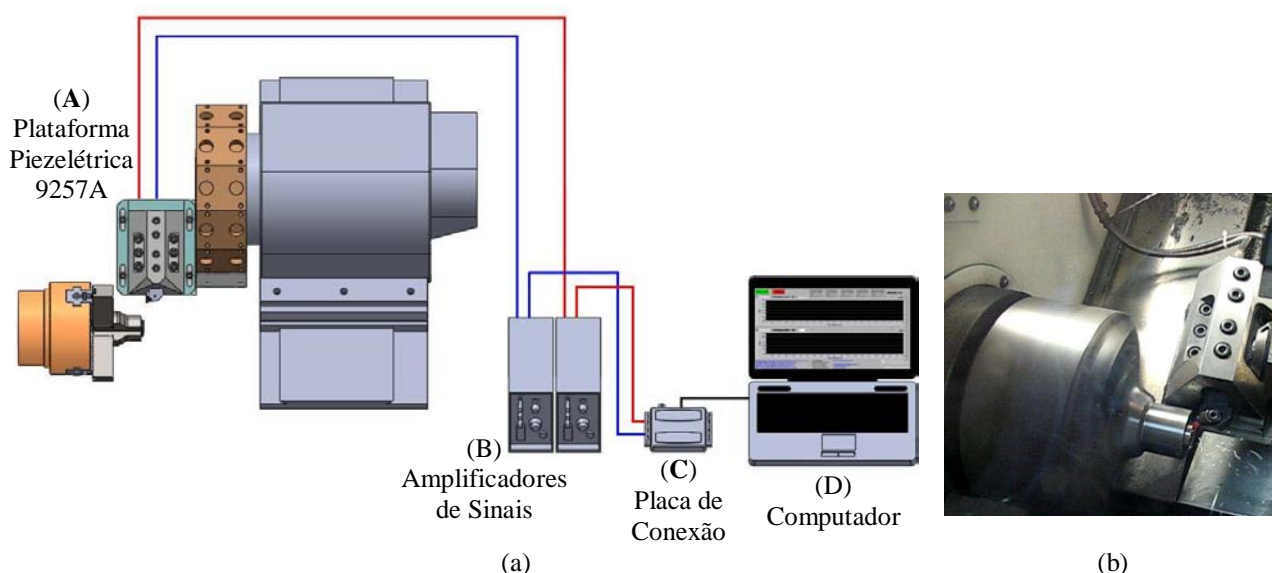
(a) Arquitetura do sistema experimental e (b) usinagem do corpo de prova.
